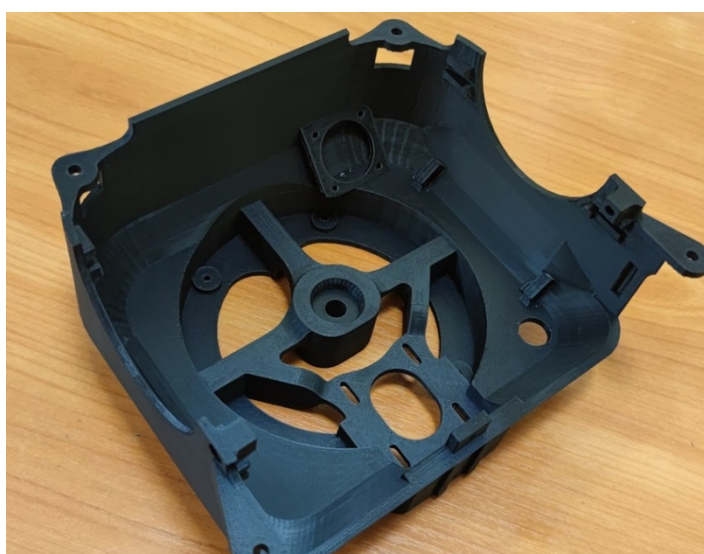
Основа робота-маніпулятора після обробки
